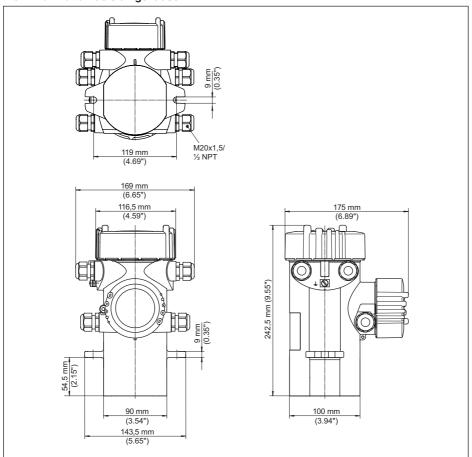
Aluminiumgehäuse bzw. Edelstahlgehäuse (Feinguss)
